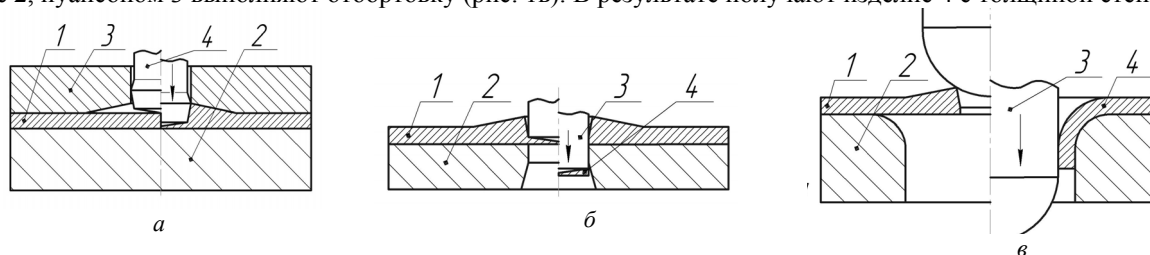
Последовательность операций получения отбортовкой изделий с толщиной стенки, которая не меньше толщины исходной заготовки: а – образование отверстия и профилирование выдавливанием исходной заготовки; б – пробивка перемычки; в - отбортовка
